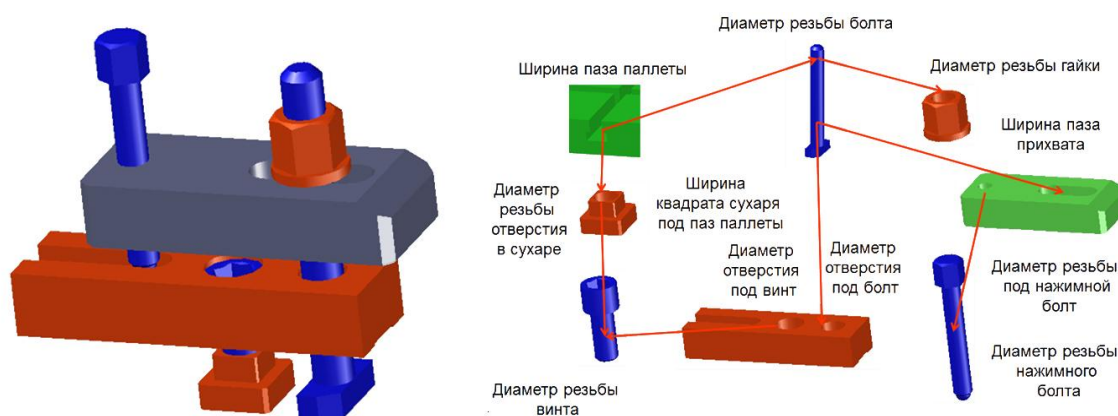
Пример связей между присоединительными поверхностями деталей типовой сборки зажимных элементов СРП
